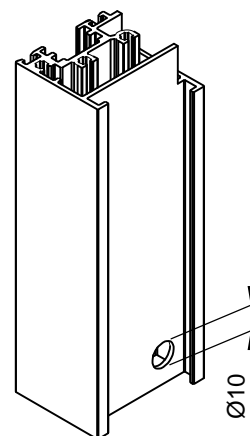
x 45. Povezivanje vertikalnog pojasa rama F-1600 i praga F-1603
